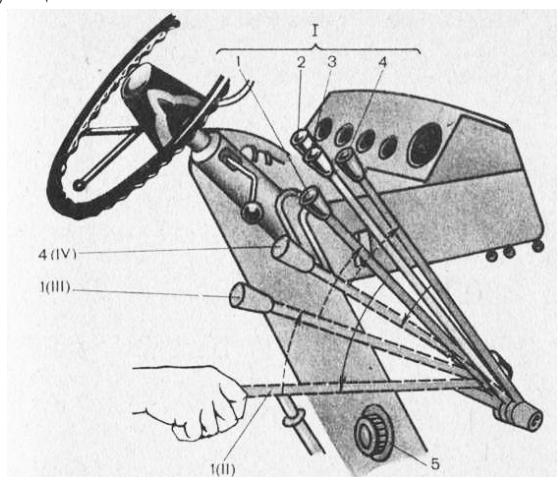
Рычаги управления гидравлическим догрузателем ведущих колес трактора: 1 - гидродогрузателя; 2, 3 и 4 - силовых цилиндров; 5 - маховичок; I...IV - положения рычагов
